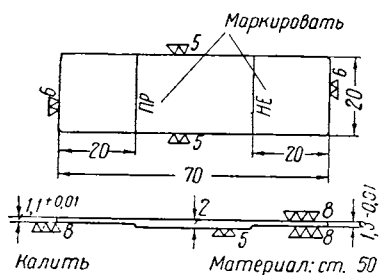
Калибр для проверки расстояния между неподвижным бортом и зубьями грейфера
